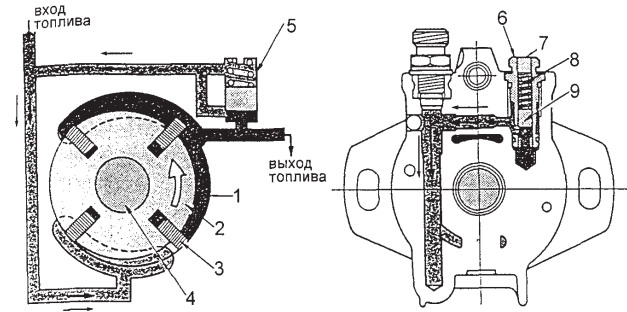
Топливный насос низкого давления и регулирующий клапан: 1 - кольцевая полость; 2 - ротор; 3 - лопасти; 4 - вал; 5 - перепускной регулирующий клапан; 6 - корпус клапана; 7 - резьбовая пробка; 8 - пружина; 9 - плунжер.
